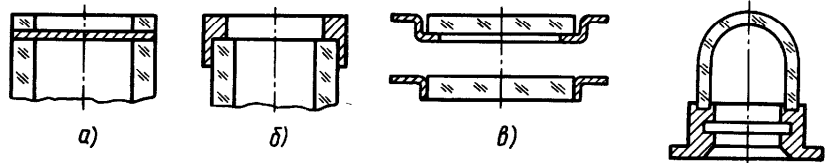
Основные типы сварных соединений стекла с металлами: а - торцовое; б - охватывающее; в - оконное; г - деталь
